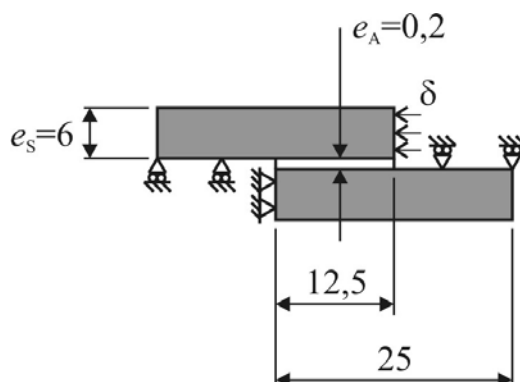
Geometria, dimensões e condições fronteira da junta *block shear* (dimensões em mm).
